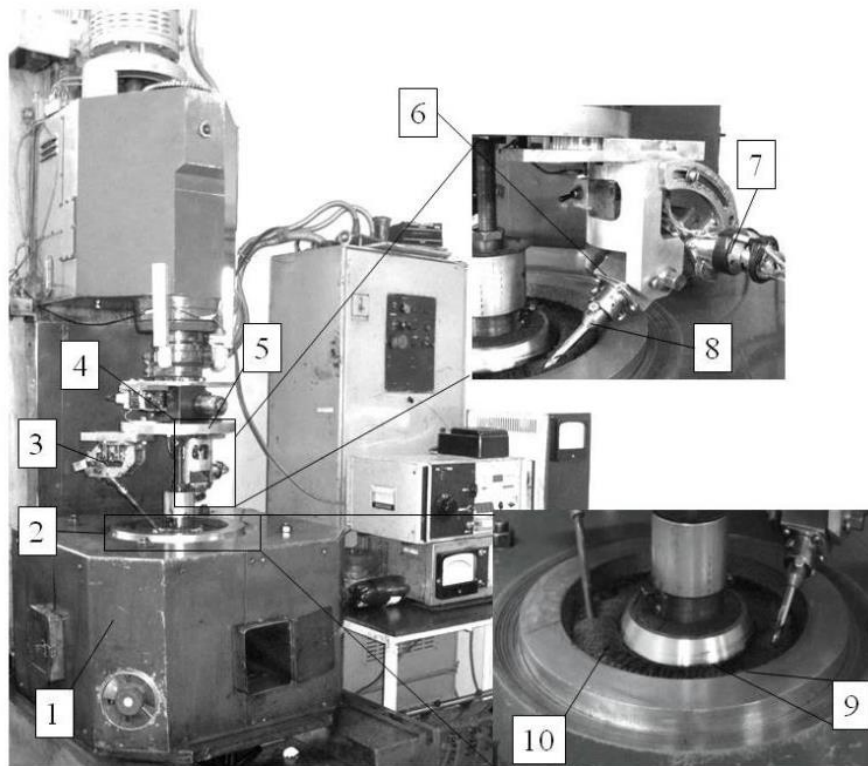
Експериментальний стенд для МАО з кільцевим розташування робочої зони: 1 – магнітна система; 2 – кільцева робоча зона; 3 – другий змінний шпиндель; 4 – універсальна головка; 5 – базова плита; 6 – пристрій з мінішпинделем; 7 – двигун постійного току; 8 – оправка з деталлю; 9 – полюсний наконечник; 10 – магнітно-абразивний інструмент.
